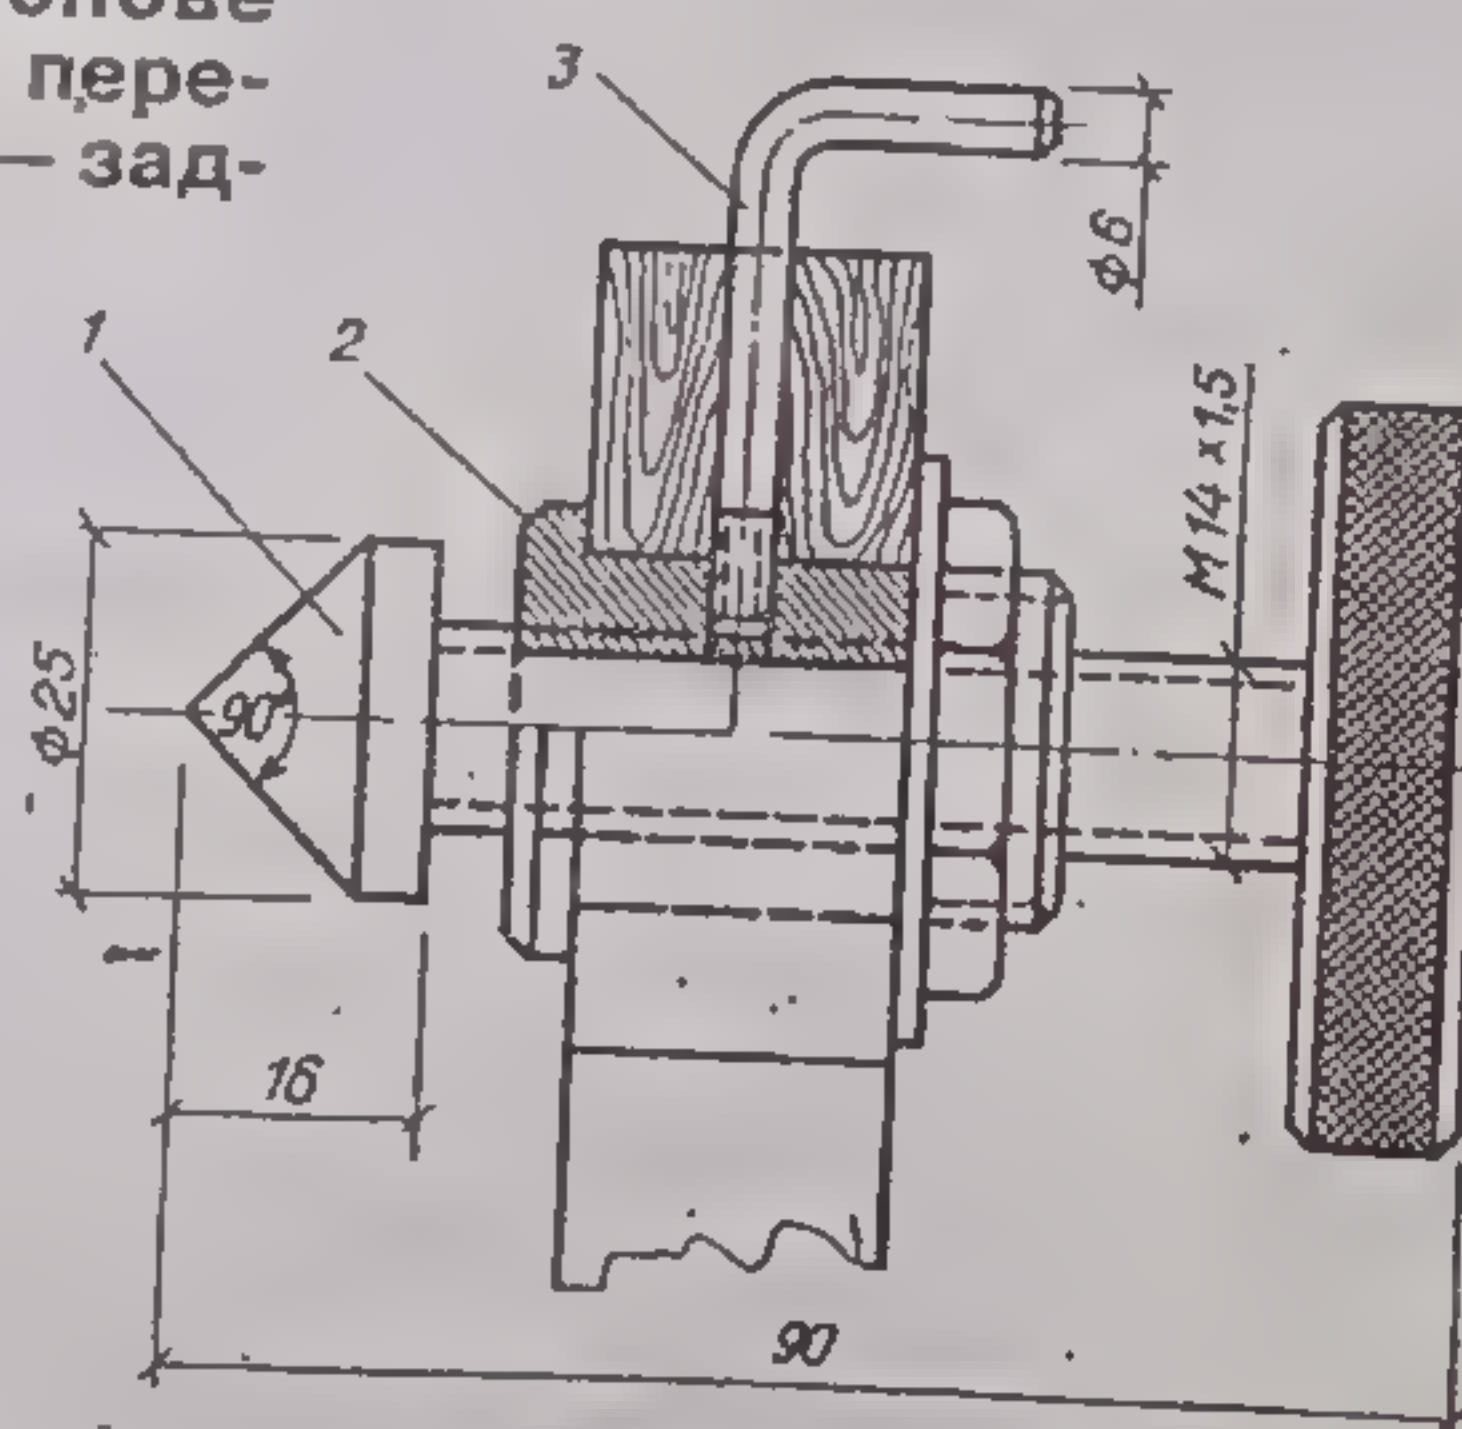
Центр задней бабки: 1 — центр; 2 — втулка; 3 — стопорный винт.
